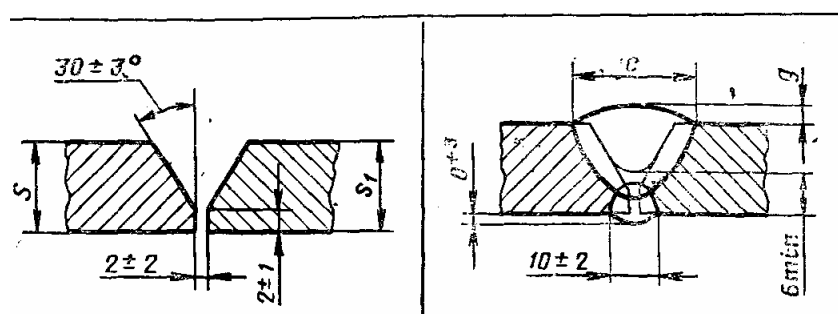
Размеры разделки и сварного шва
